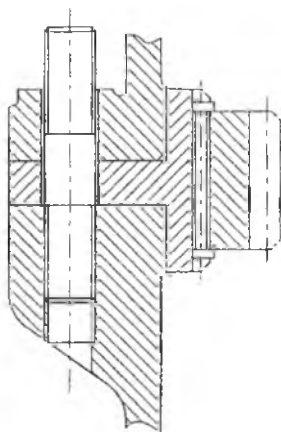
Центрирование корпусов внешм неподвижного колеса
